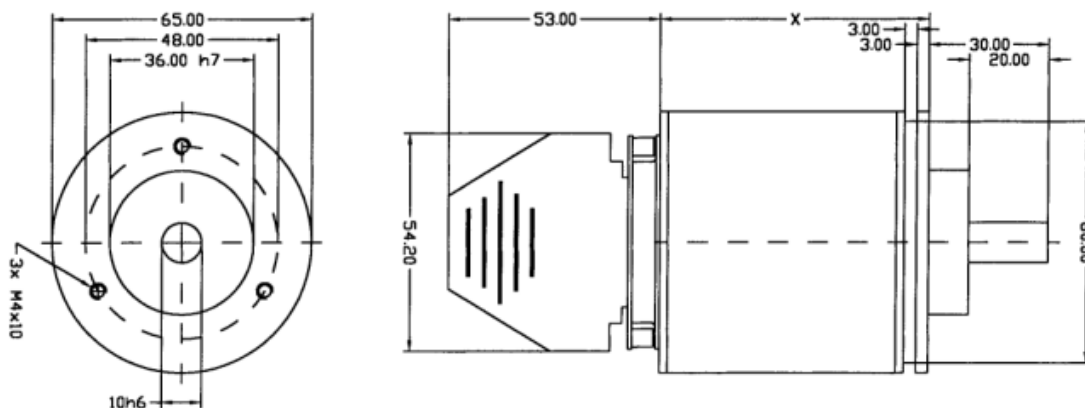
Maßzeichnung ROTARNOCK RS232 oder RS485 oder PROFIBUS, Ausführung IP54
